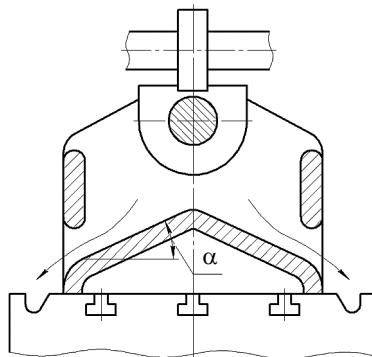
Корпус приспособления с элементами для отвода СОТС и стружки
